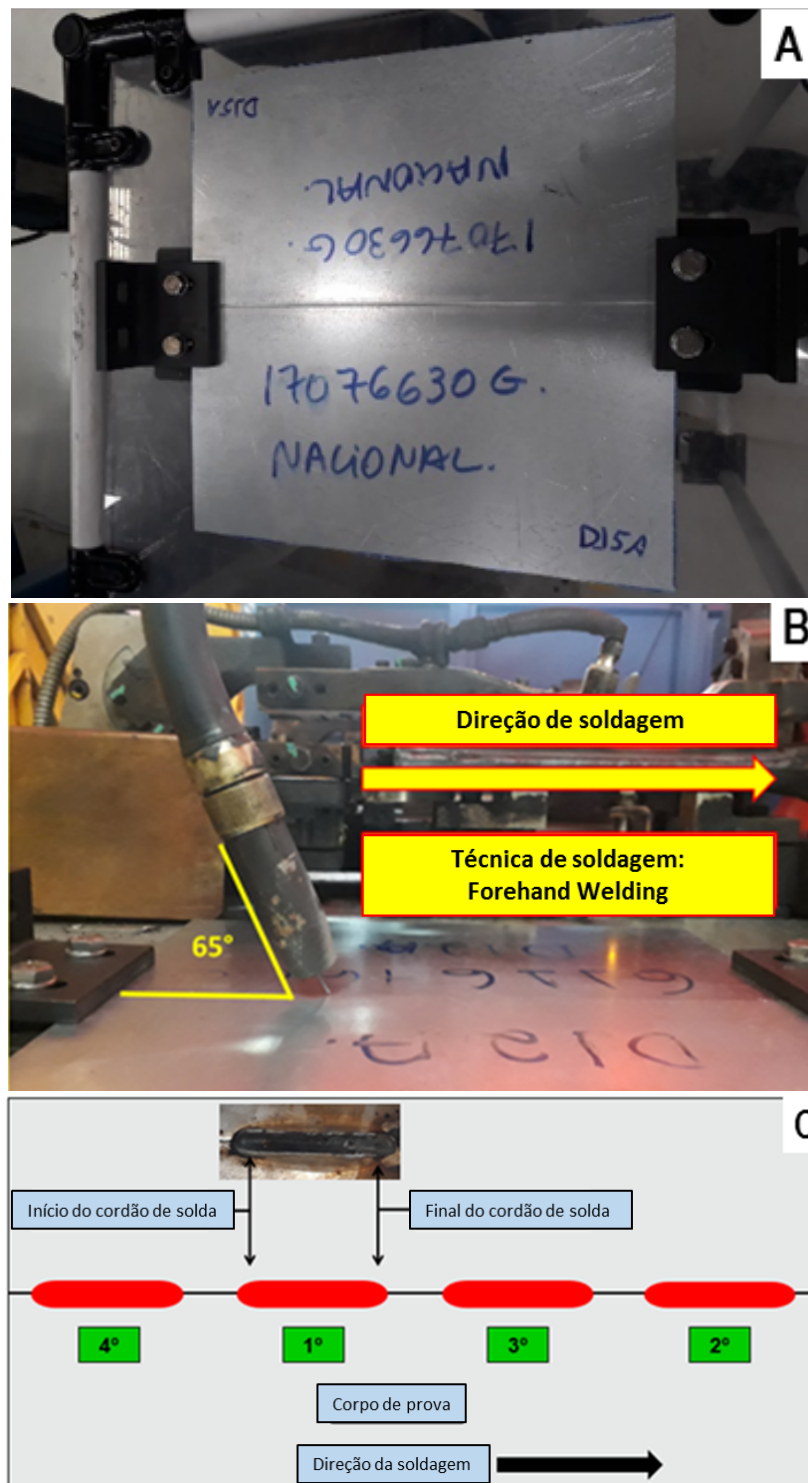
Conjunto usado na soldagem das amostras investigadas.
